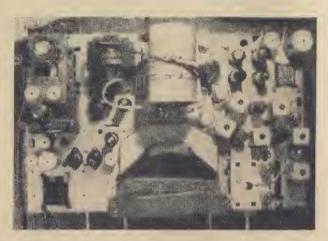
Aufsicht auf das Chassis ohne Bildröhre. Lage der Teile vgl. mit Bild 6
